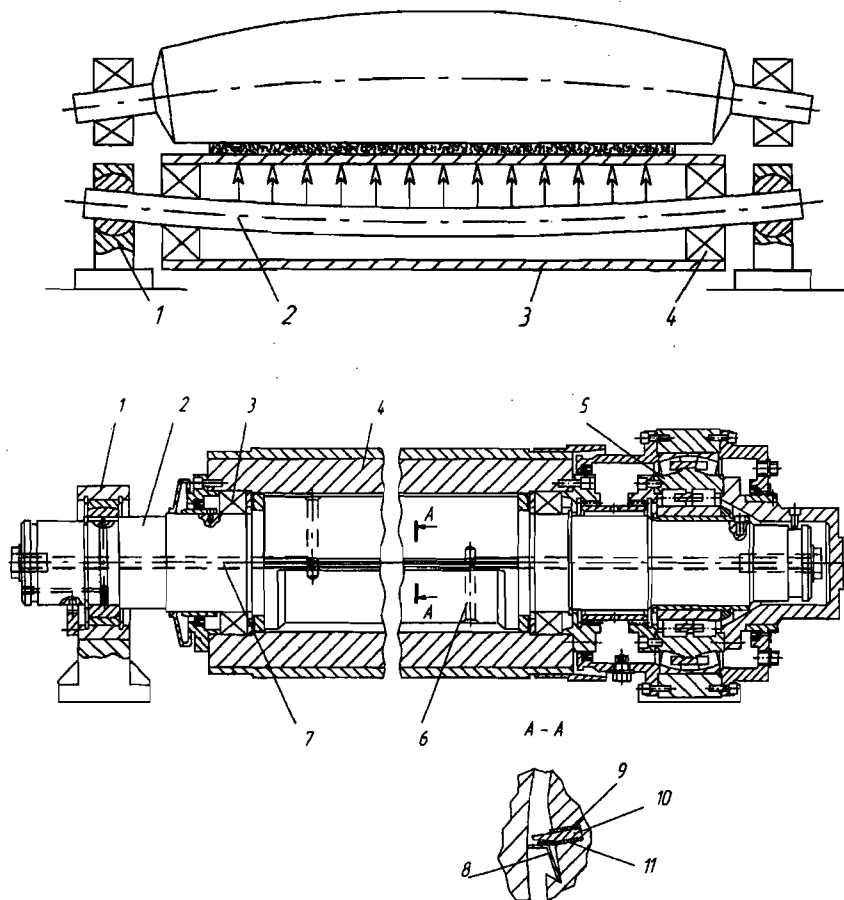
Регулирование распределения давления с помощью вала Кюстера: а – схема прессы с валом Кюстерс: 1 – опора сердечника; 2 – сердечник; 3 – рубашка; 4 – подшипник рубашки; б – вал Кюстера: 1 – опора сердечника; 2 – сердечник; 3 – подшипник рубашки; 4 – рубашка вала; 5 – трехкольцевой подшипник; 6 – канал для отвода масла из нерабочей камеры; 7 – канал для подвода масла в напорную камеру; 8 – уплотнительная планка; 9 – уплотнительная лента; 10 – опорная планка; 11 – пружинная лента
